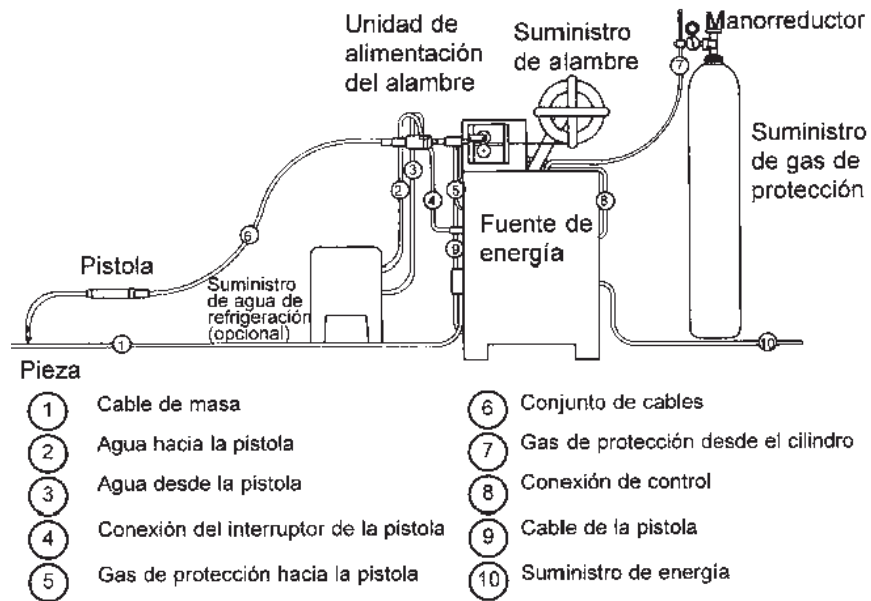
Equipo necesario para el proceso de soldadura GMAW
